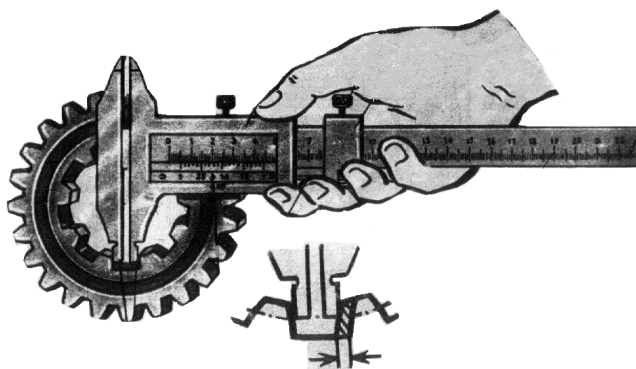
Схема измерения ширины паза ступицы штангенциркулем.
